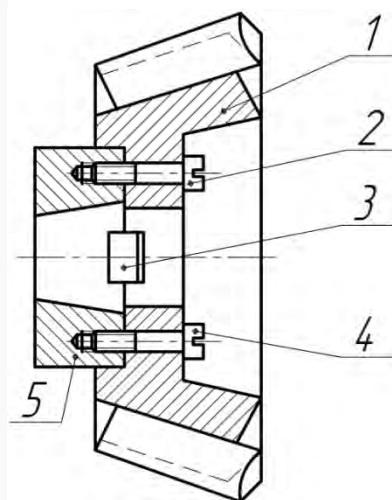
Закрепление насадных торцевых фрез непосредственно на шпинделях станка
